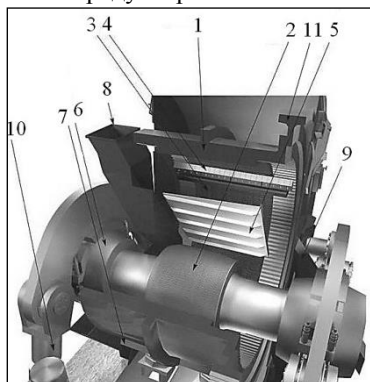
Конструкция горизонтальной валковой мельницы Honomill: 1 – цилиндрический корпус; 2 – вал; 3 – опорный подшипник; 4 – скребки; 5 – система регулирования скорости подачи материала; 6 – шарнир; 7 – гидродинамические подшипники скольжения; 8 – входной патрубок; 9 – выходной патрубок; 10 – гидроцилиндр; 11 – венцовый привод
